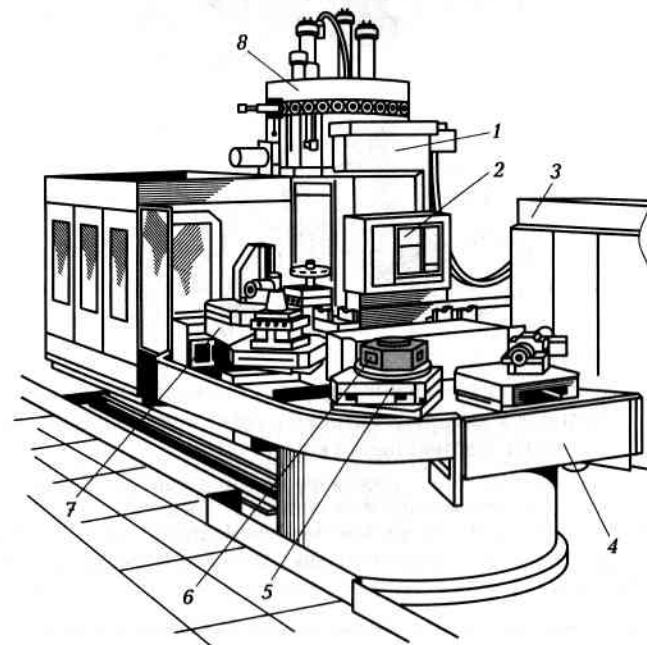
Многооперационный станок с ЧПУ для обработки корпусных деталей:
